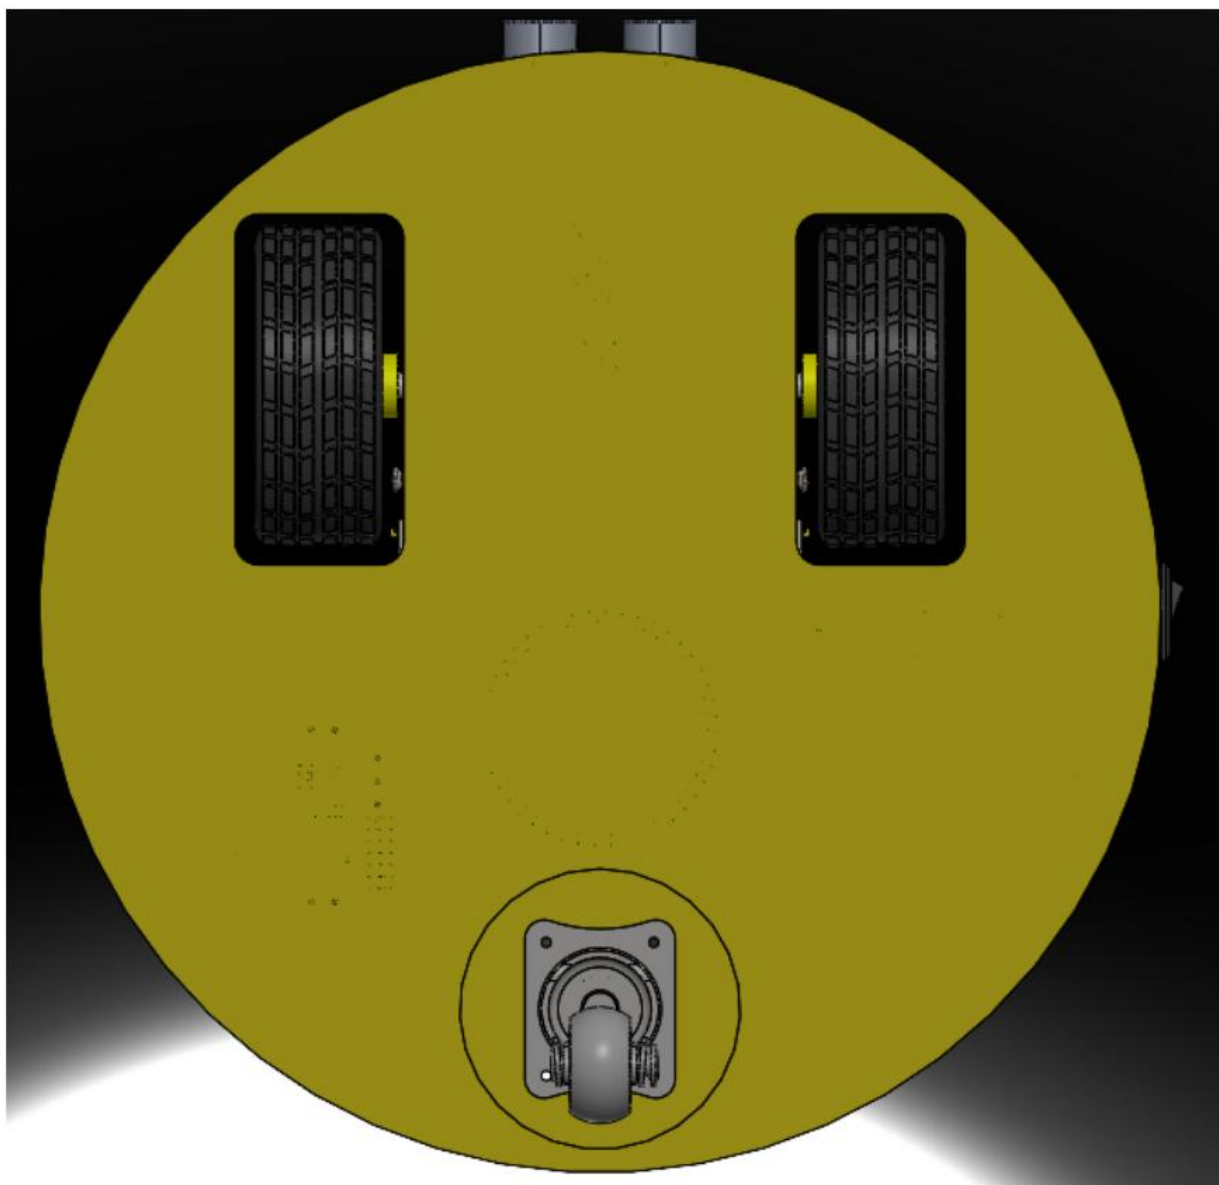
Вид знизу. Шасі, ведучі колеса та опорний ролик
